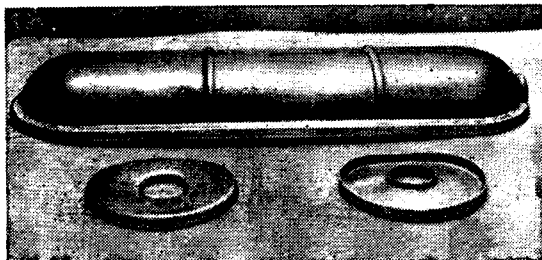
Детали глушителя автомобиля «Москвич-408», изготовленные из алюминированной стали
